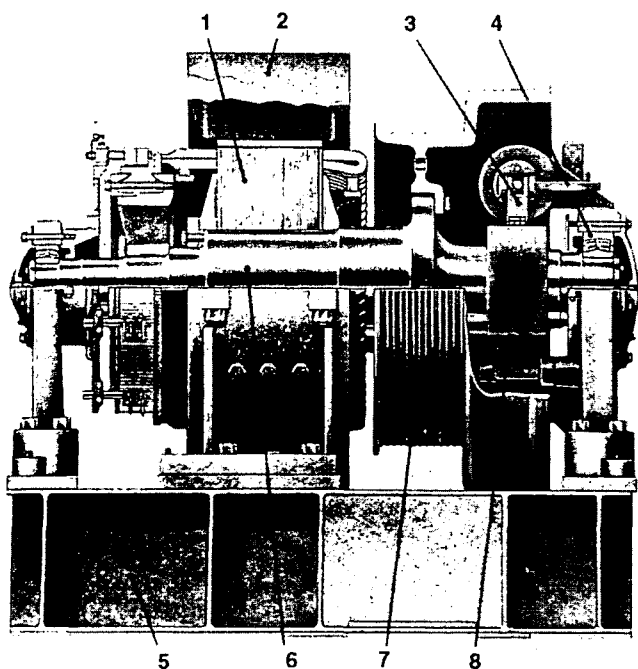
Продольный разрез безредукторной лебедки (Otis Elevator Co.): 1 – ротор, 2 – статор, смонтированный на опорной плите, 3 – механический тормоз внешнего типа, 4 – самоустанавливающиеся роликовые подшипники, расположенные на концах вала так, что все вращающиеся компоненты лебедки установлены на валу между подшипниками, 5 – сварная конструкция опорной плиты, 6 – кованный стальной вал, 7 – тяговый шкив, отлитый вместе с тормозным шкивом и закрепленный болтами на фланце вала, 8 – тормозная колодка
